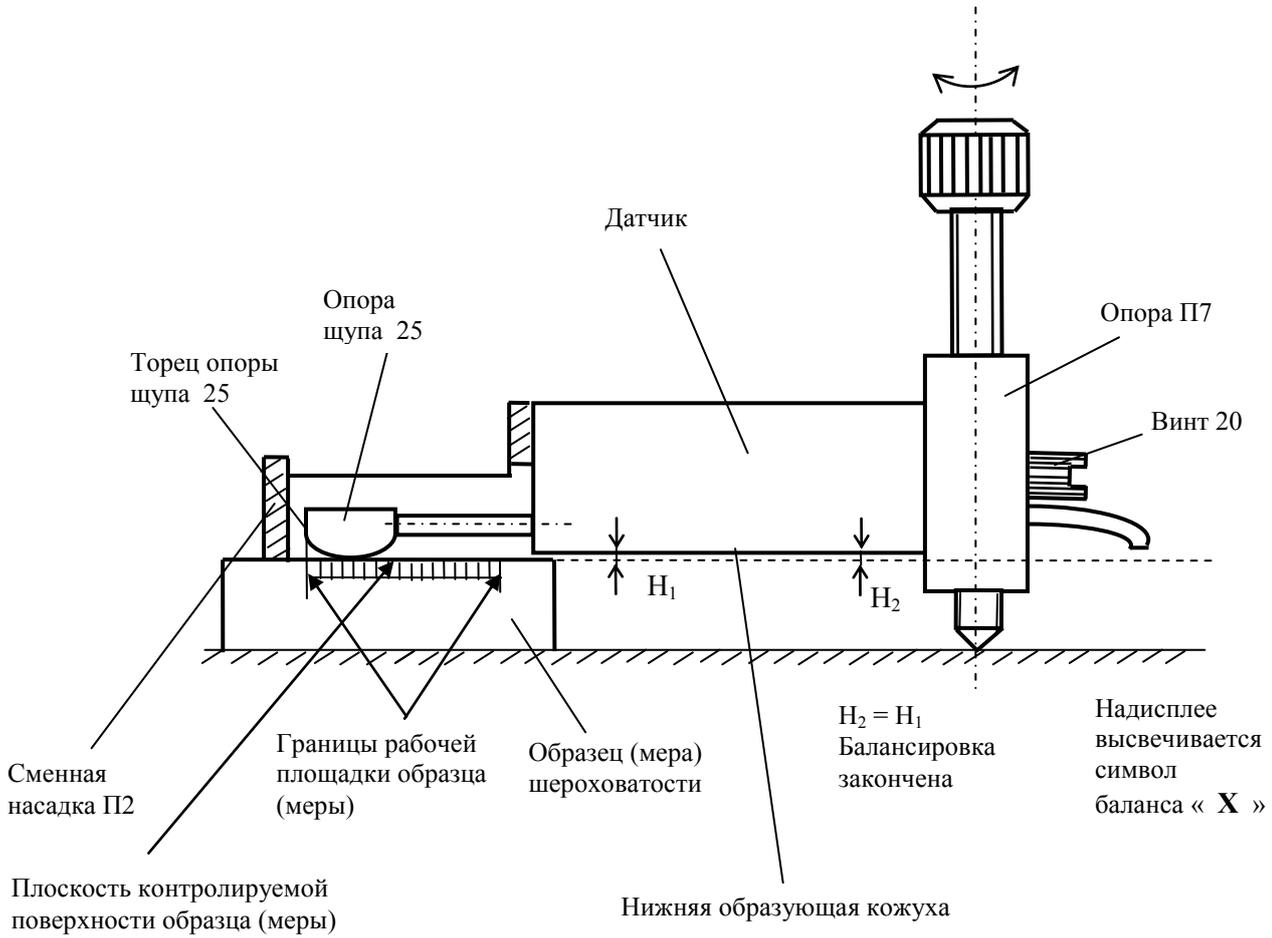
Базирование датчика на поверхность образца (меры) шероховатости с помощью опоры П7. Положение по окончании балансировки. Вид сбоку.
